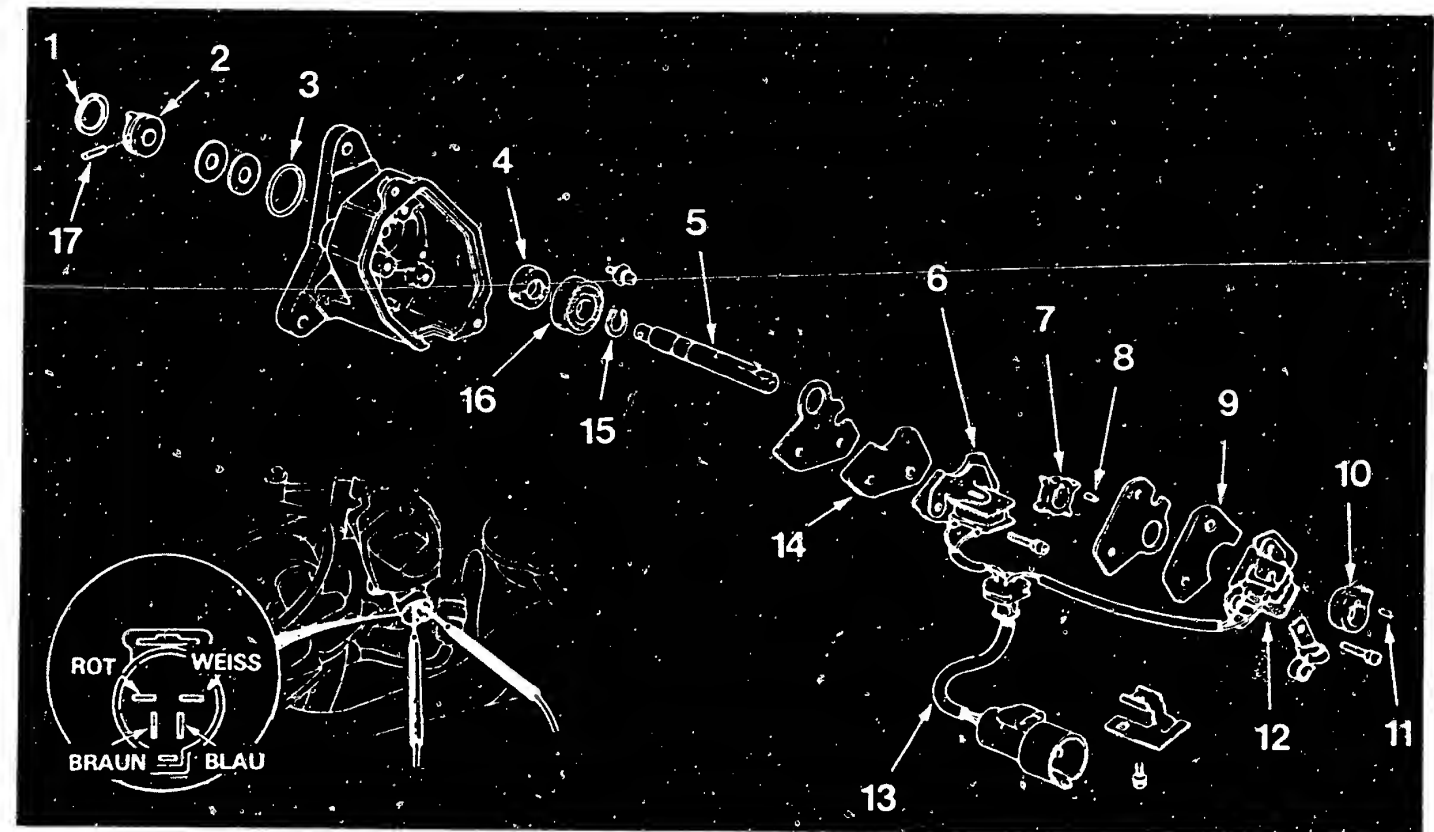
Einzelteile des Kurbelwinkelsensors. Die Prüfwerte am Steckanschluss (Einsatz links) sind im Textteil zu finden. 1 Haltering – 2 Kupplungsstück – 3 O-Ring – 4 Dichtring – 5 Rotorwelle – 6 Spulensatz (TDC) – 7 Rotor – 8 Stift – 9 Magnet A – 10 Trommelrotor – 11 Stift – 12 Trommelspulensatz – 13 Spulensatz – 14 Magnet B – 15 Seegerring – 16 Kugellager – 17 Stift.
